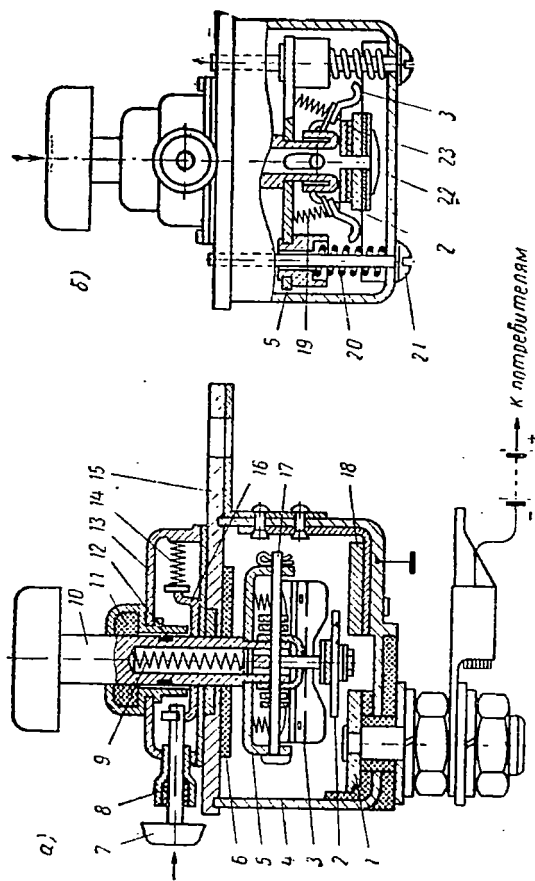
Выключатель аккумуляторной батареи ВК-318:
